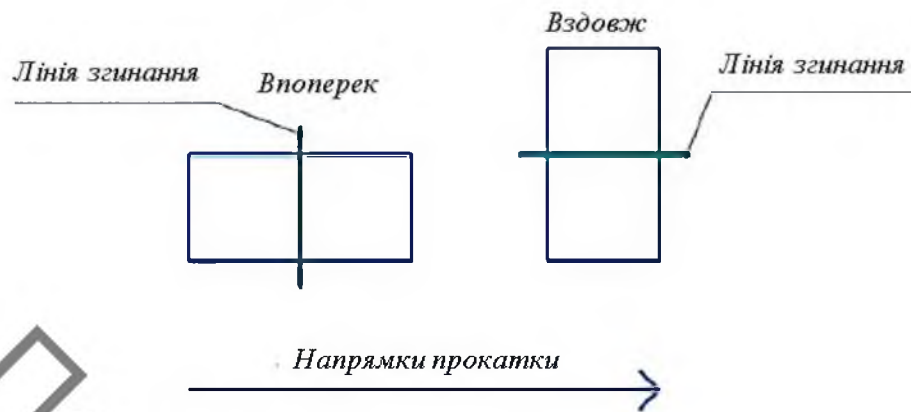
Напрямок згинання щодо напрямку прокатки заготовки
